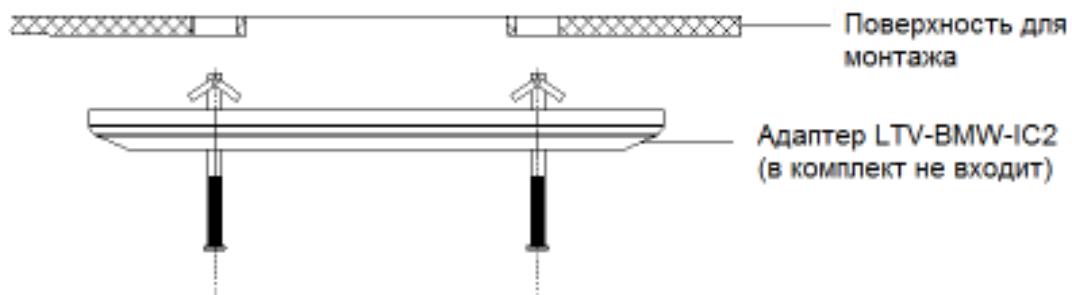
Крепление адаптера LTV-BMW-IC2 на потолок / стену
